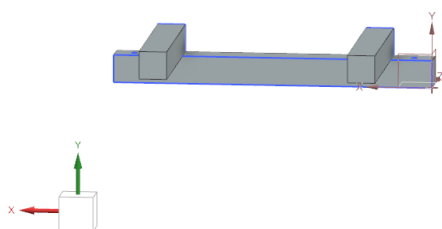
Vista isometrica dall'alto del traversino strutturale.
